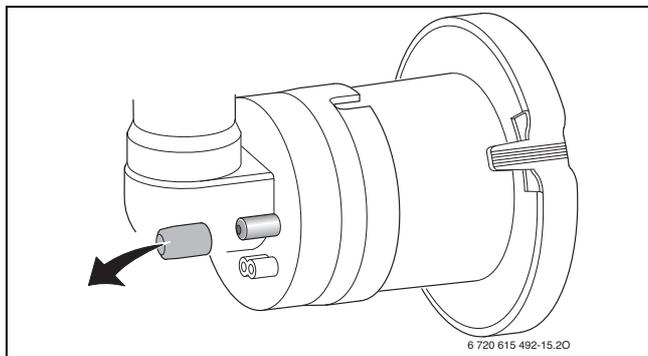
Tubulure de mesure sur le dispositif de mélange
